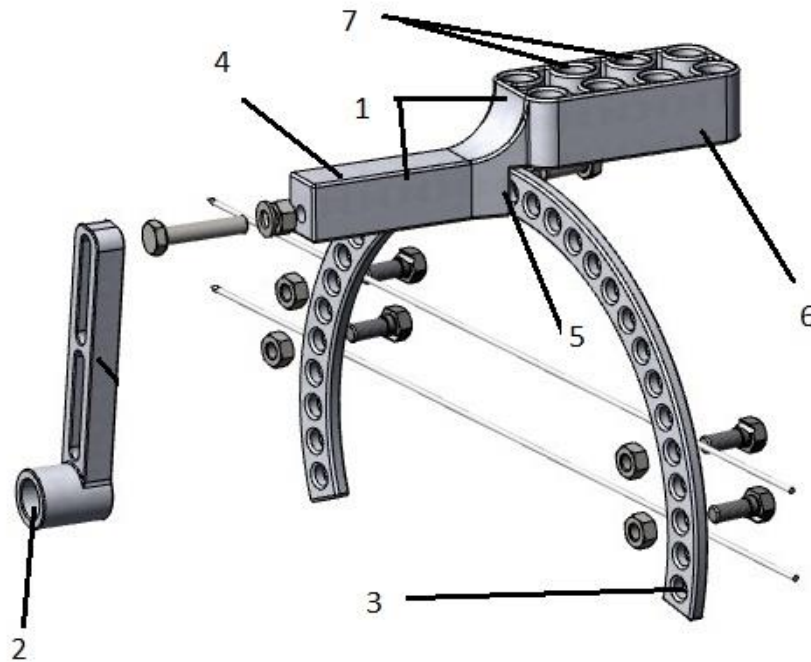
Общая схема устройства. Обозначение: 1 - рама-направитель; 2- консольный направитель; 3- опора-ориентир; 4 — базовая часть; 5 - фиксирующий паз; 6 — кондукторная ветвь; 7 — кондукторные каналы.
